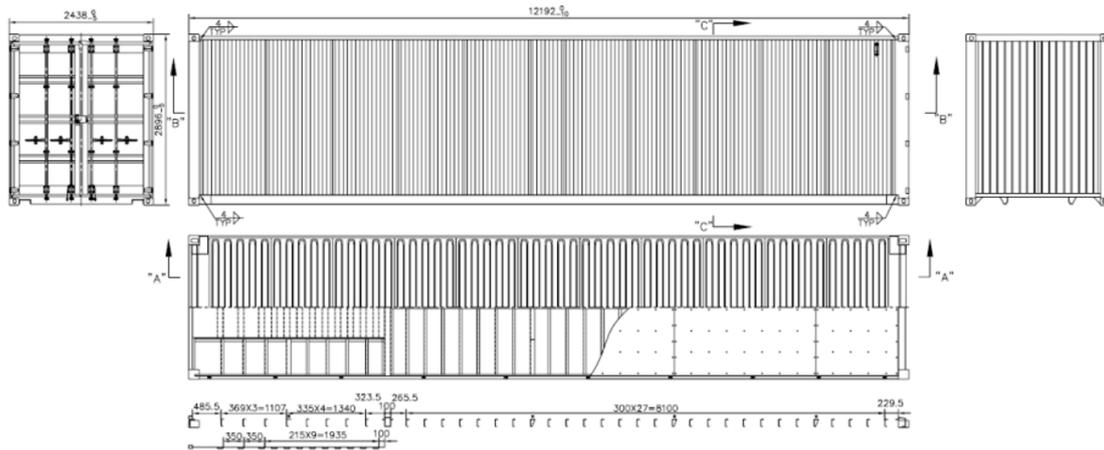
Diseño de prefabricados de sistemas de almacenamiento. (Ficha técnica fabricante).
